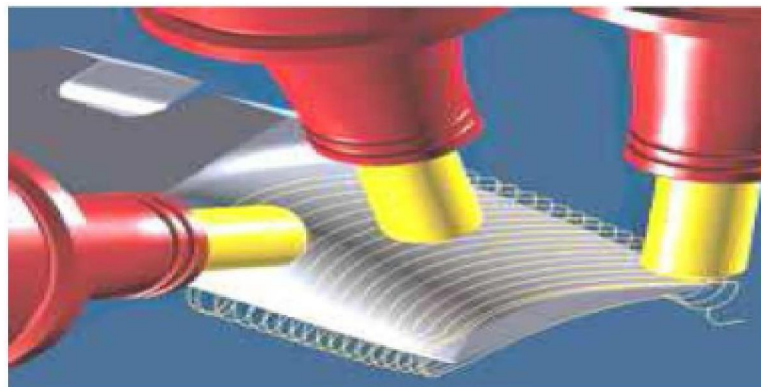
Usinage en bout d'aube de turbine 5 axes. [07]
